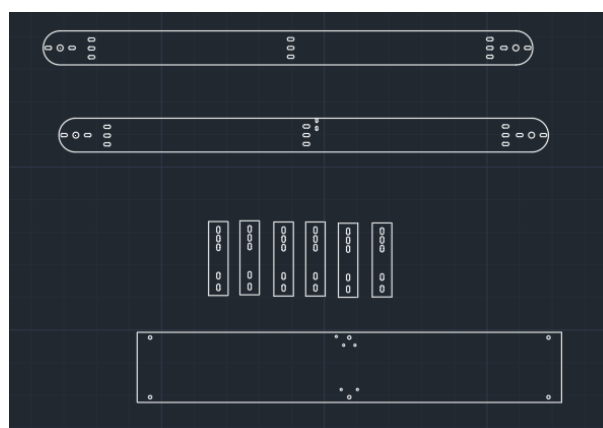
Archivo para realizar el corte de la plancha (Banda)
